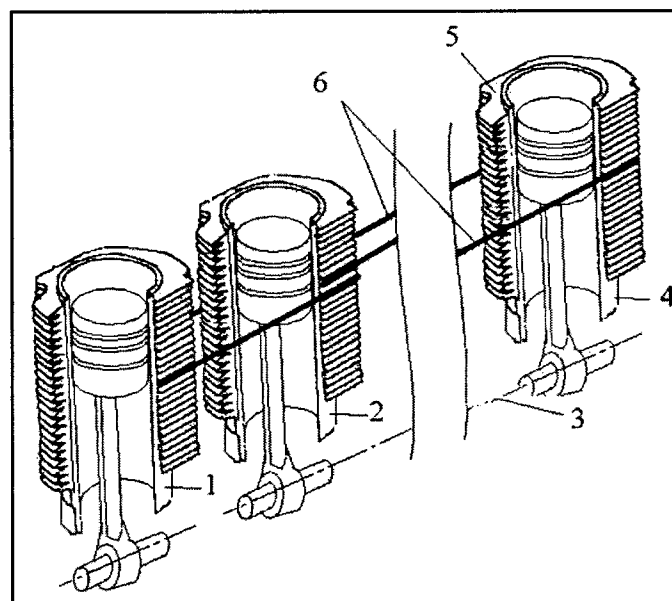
Альтернативная конструкция блока двигателя с воздушным охлаждением:
